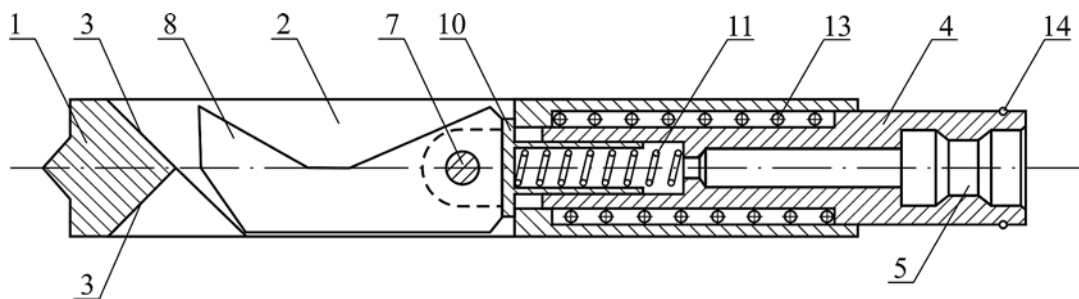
Схема щелеобразователя разработки ФГБУ «Институт угля СО РАН»: 1 – стакан; 2 – продольное окно; 3 – перекрестные оппозитные направляющие уклоны; 4 – толкатель; 5 – резьбовое отверстие; 6 – проушины; 7 – ось; 8 – режущий орган; 9 – торцовая часть режущего органа; 10 – направляющая втулка; 11 – пружина; 12 – отверстие; 13 – пружина возврата; 14 – упорное кольцо
